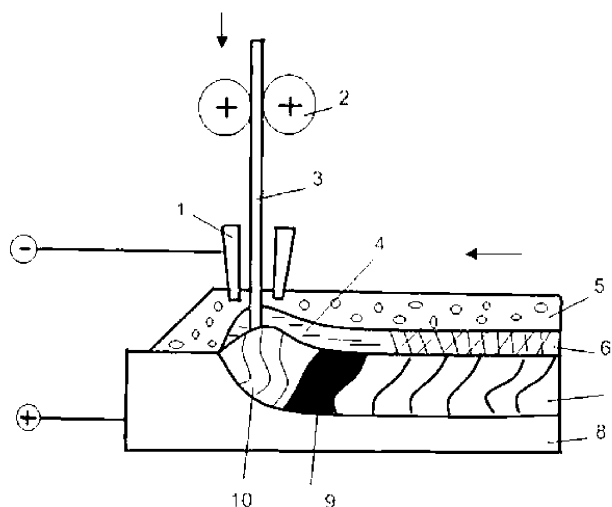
Схема сварки под флюсом:
